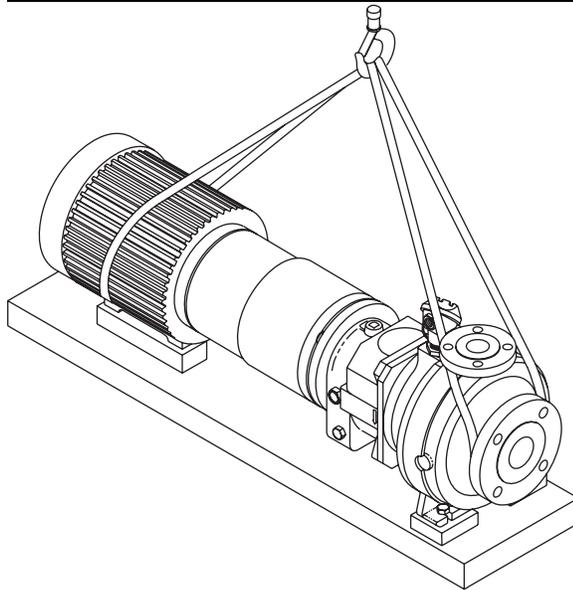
Metodo di sollevamento corretto per una pompa con base e motore
